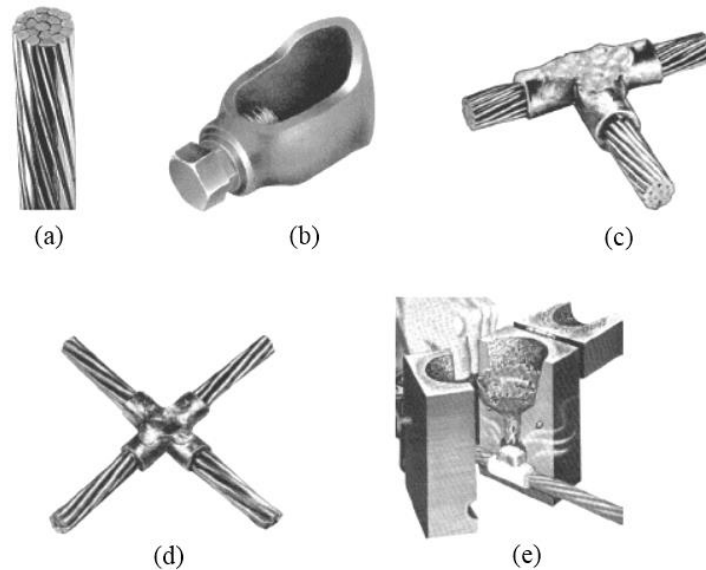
Acessórios para a rede de aterramento. (a) Condutor. (b) Conexão aparafusada. (c) Solda exotérmica tipo "T". (d) Solda exotérmica tipo "X". (e) Cadinho de solda [17].
